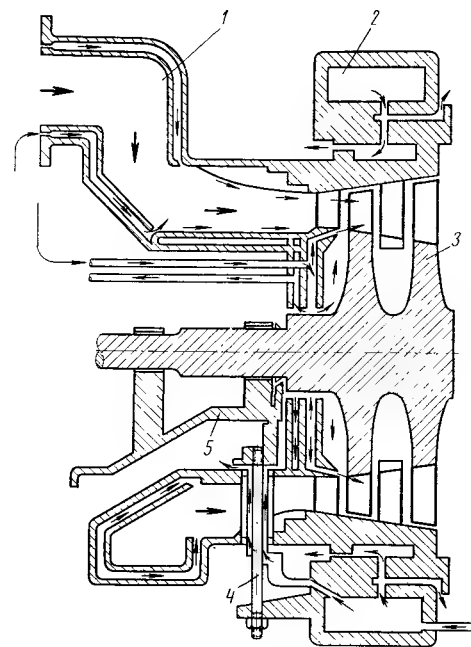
Схема крепления корпуса подшипника ГТУ мощностью 5500 квт фирмы Кларк:
